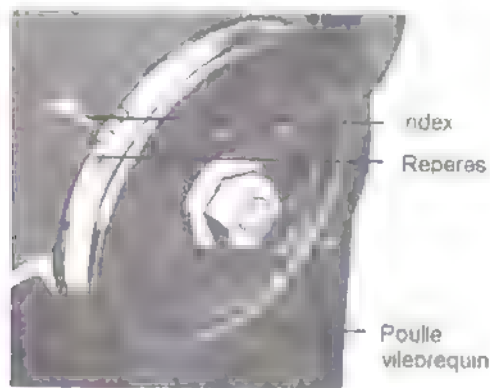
Repère mobile sur poulie en bout de vilebrequin.
